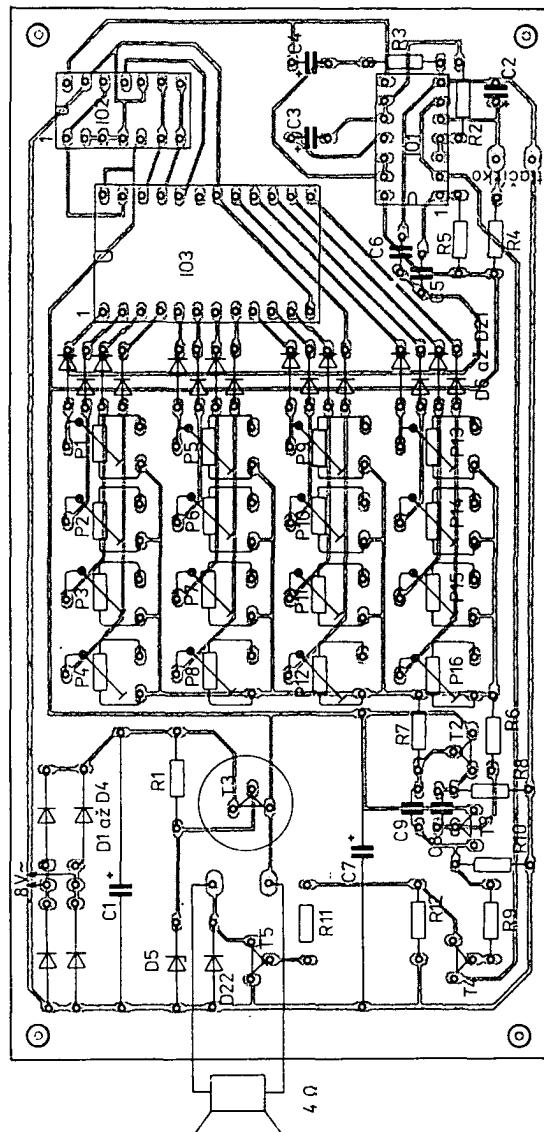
Obrazec plošných spojů k obr. 1a (R52)
